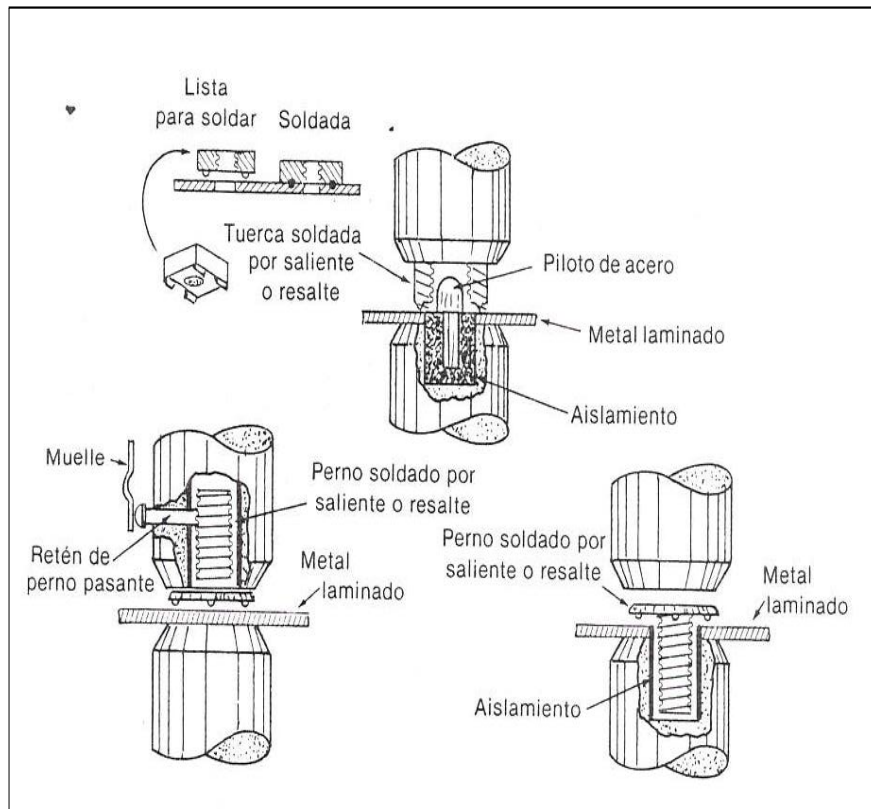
Ejemplos de tuercas y tornillos soldados por proyección.
